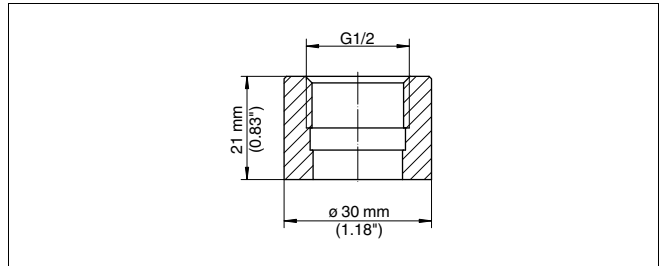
Medidas racor soldado rosca G $\frac{1}{2}$  B según ISO 228-1 - tubería
